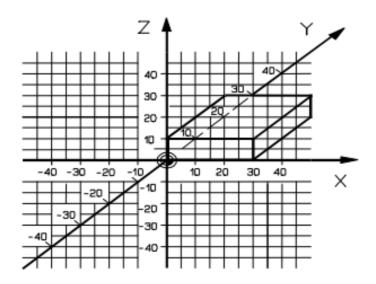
Расположение нулевой точки Wна фрезерном станке с ЧПУ
